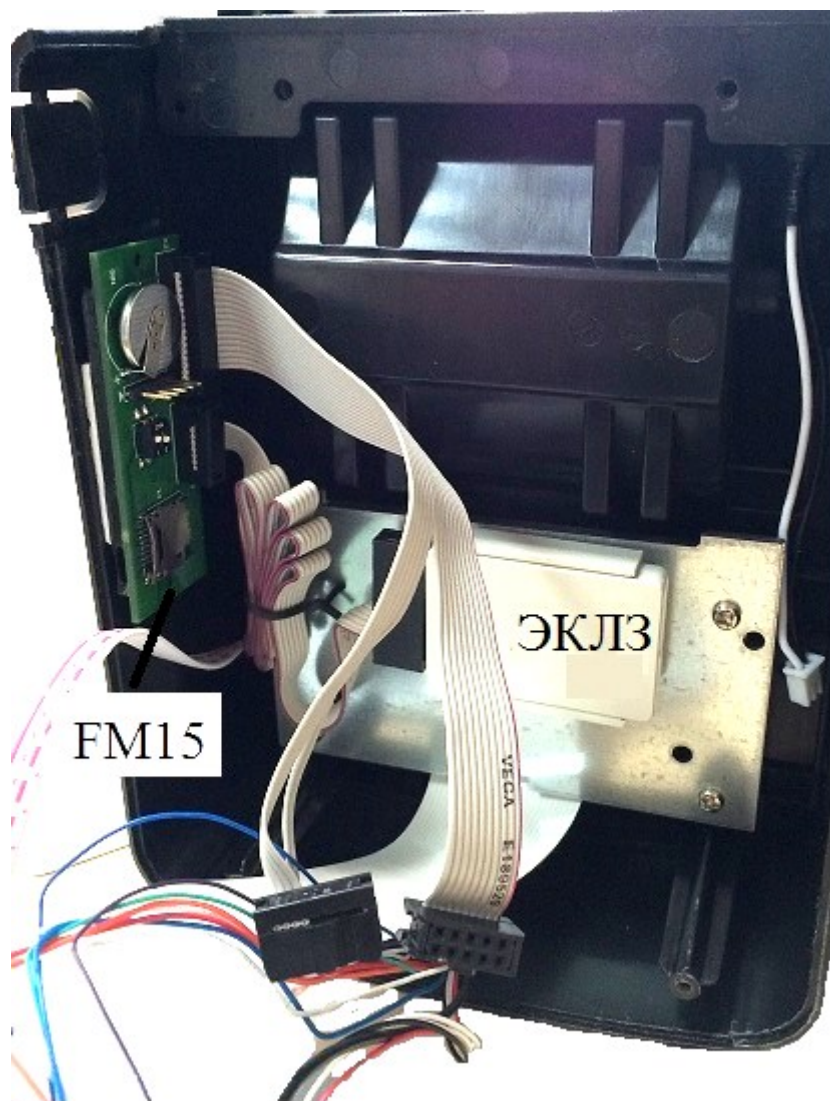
Крепление ФП и ЭКЛЗ к корпусу основного блока ПТК
